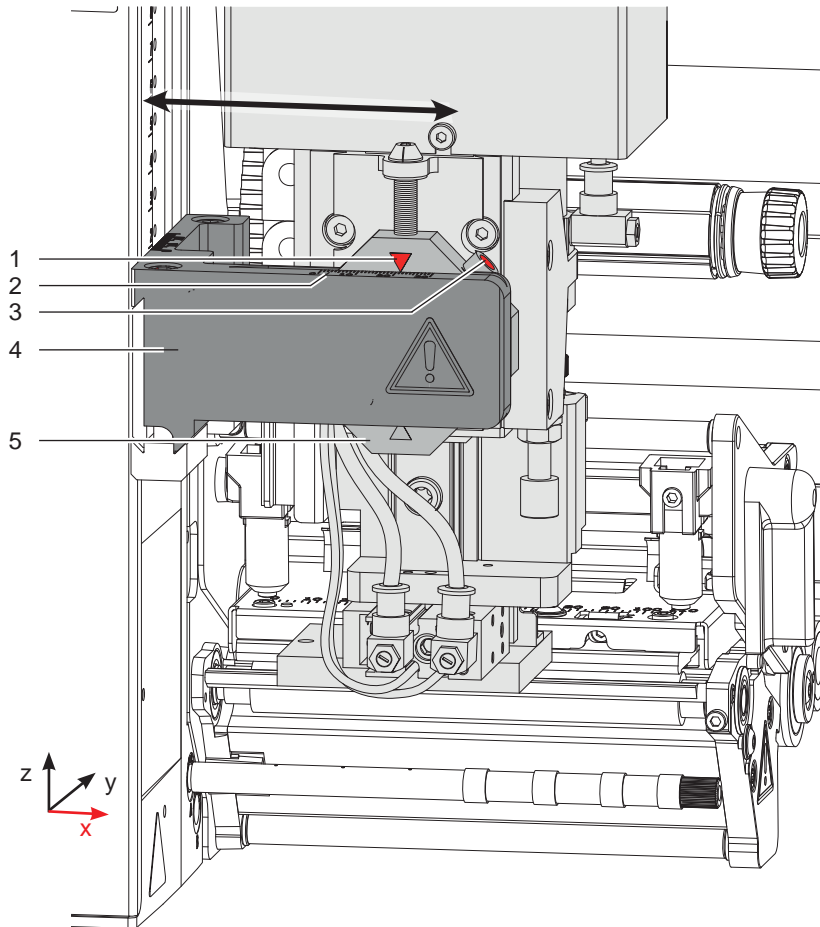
Verschiebung der Stempelbaugruppe in X-Richtung
